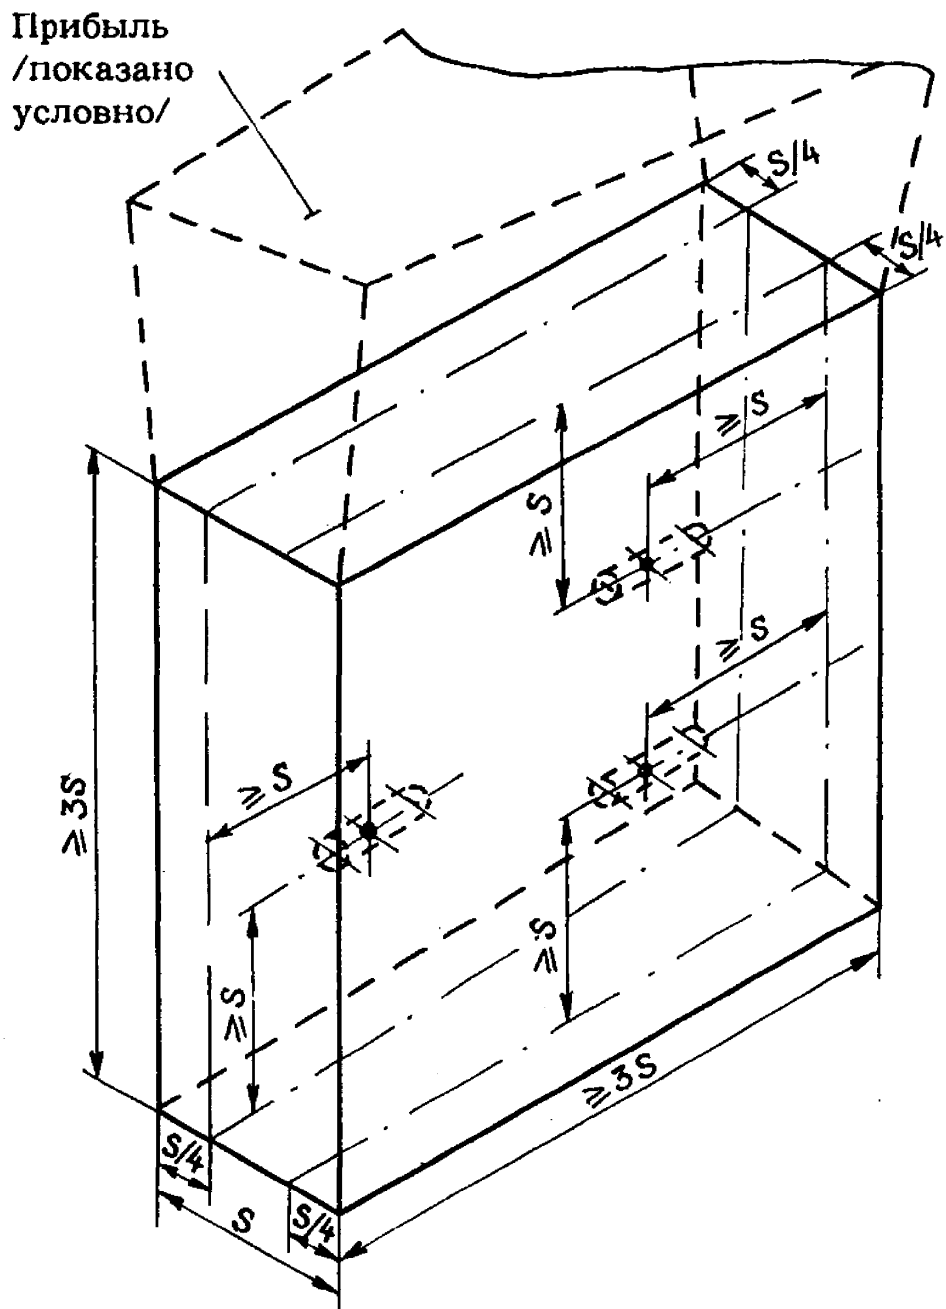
Схема отбора образцов для испытаний механических свойств из отдельно отлитой пробы
